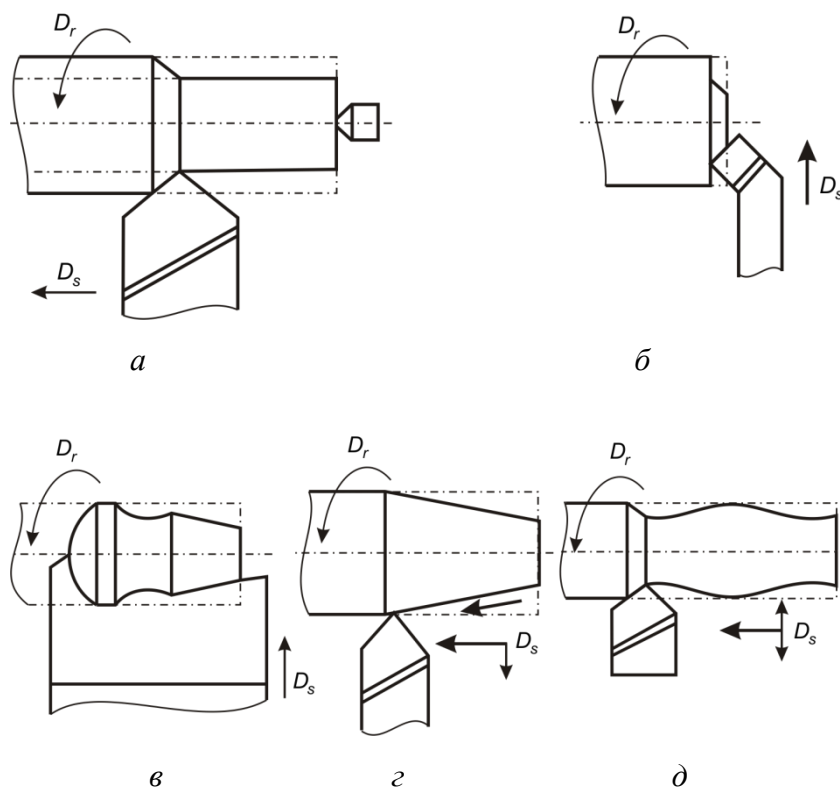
Главные движения резания и движения подачи при обработке различных поверхностей деталей точением:
